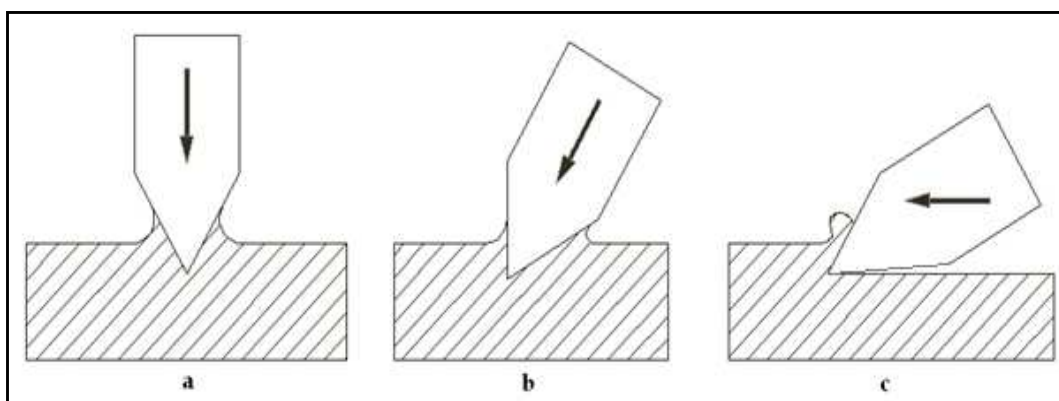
Posiciones de la herramientas y direcciones de la fuerza⁹
